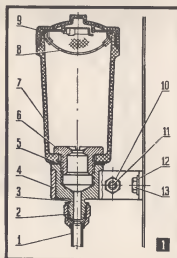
Установка нового бачка: 1 — трубопровод, идущий к главному цилиндру; 2 — наливная гайка; 3 — переходник; 4 — хомут; 5 — резиновая прокладка; 6 — штуцер; 7 — наполнительный бачок; 8 — сетка; 9 — крышка; 10 — гайка М6; 11 — болт М6х26; 12 — зубчатая шайба (2 штуку); 13 — болт М6х14 (2 штуку).
